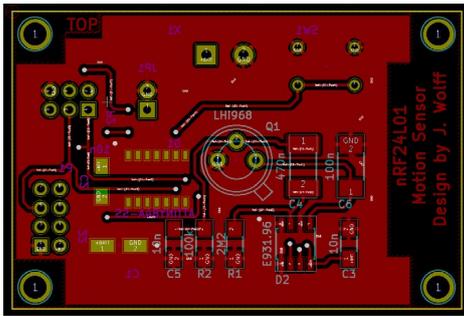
PCB del sensor de movimiento nRF24 - parte superior
